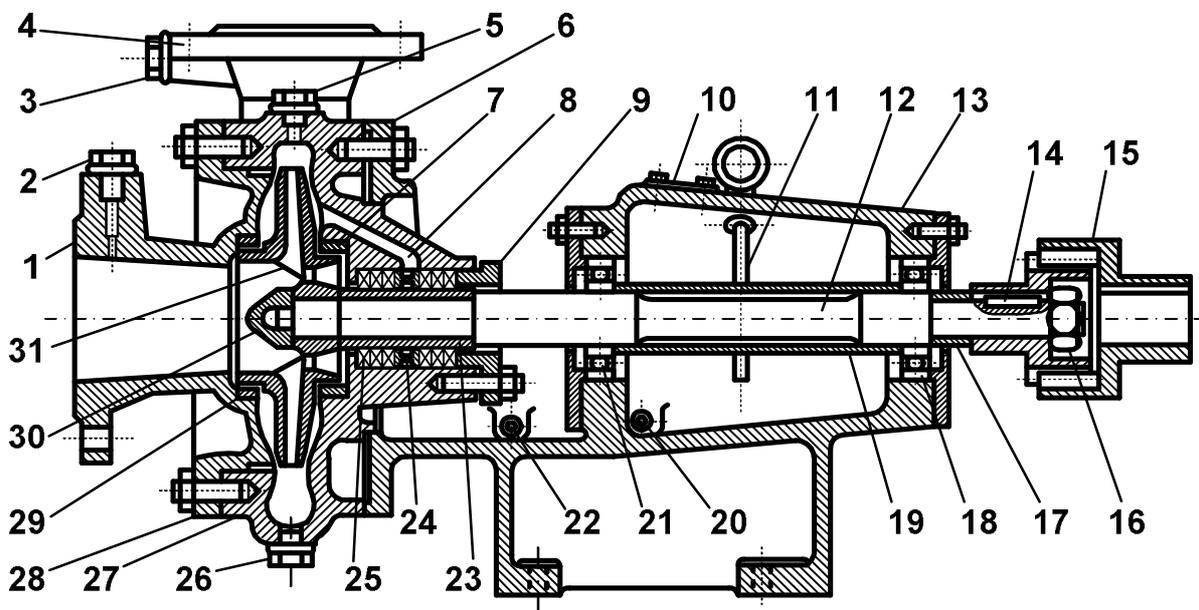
Консольный насос типа К: 1 и 4 – всасывающий и нагнетательный патрубки; 2 и 3 – гнезда для установки вакуумметра и манометра; 5 и 26 – верхняя и нижняя пробки корпуса; 6 – опорный фланец для корпуса насоса; 7 и 29 – кольцевые уплотняющие втулки; 8 – канал гидрозатвора сальника; 9 – фланец сальника; 10 – крышка камеры подшипников; 11 – щуп; 12 – вал; 13 – камера подшипников; 14 – шпонка; 15 – соединительная муфта; 16 – стопорная гайка полумуфты; 17 и 19 – дистанционные втулки; 18 – задний радиально-упорный подшипник; 20 – сливное отверстие для масла; 21 – передний радиальный подшипник; 22 – дренажное отверстие; 23 – защитная втулка;
